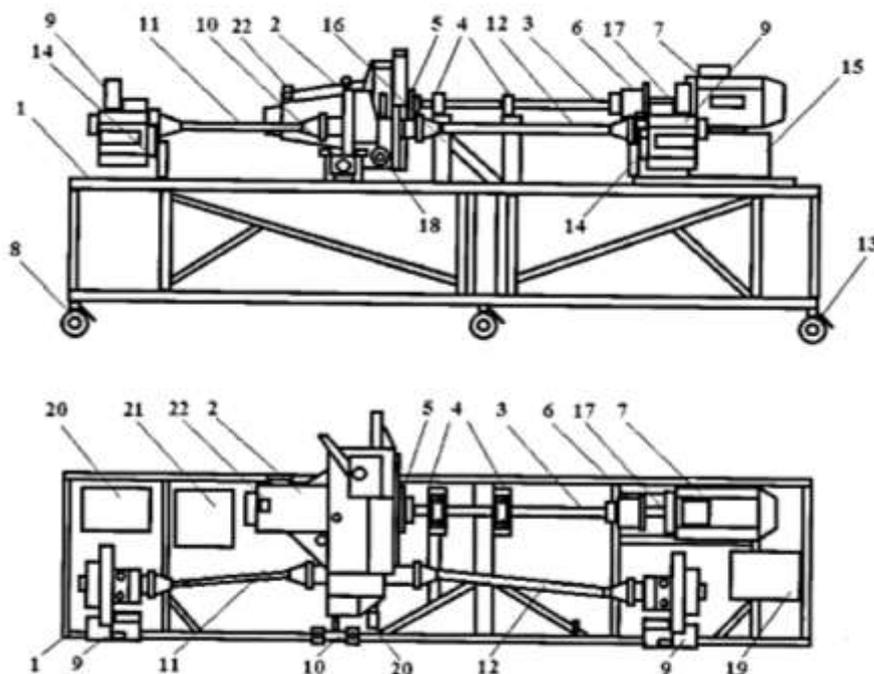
Конструкция экспериментальной установки: 1 – монтажная рама; 2 – коробка передач; 3 – приводной вал; 5 – муфта; 4 – опора; 6 – гибкая муфта; 7 – электродвигатель; 8 – колеса; 9 – механизм загрузки коробки передач; 10 – гибкая опора; 11 – приводной вал; 12 – приводной вал; 13 – тормозные механизмы; 14 – опора; 15 – кронштейн; 16 – кронштейн; 17 – вал; 18 – механизм переключения передач; 19 – блок управления электродвигателем; 20 – блок управления гидравлическим приводом; 21 – блок преобразования сигнала; 22 – датчик вибрации
